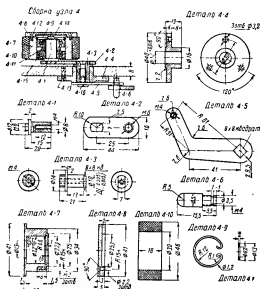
Прижимной ролик (узла 4) и его детали: 4-1—ось (сталь 45)—1 шт.; 4-2—малый рычаг (сталь 20-листовая толщиной 2 мм)—1 шт.; 4-3—ось рычага (сталь 45)—1 шт.; 4-4—подшипник (сталь 25)—1 шт.; 4-5—большой рычаг (сталь 20-листовая толщиной 2 мм)—1 шт.; 4-6—палец (сталь У8А)—1 шт.; 4-7—стакан (сталь 25)—1 шт.; 4-8—крышка (сталь 25)—1 шт.; 4-9—опорное кольцо (пруж. сталь марки Н)—1 шт.; 4-10—кольцо (резина средней твердости)—1 шт.; 4-11—распорное кольцо (сталь 3)—1 шт.; 4-12—винт М2×8 мм (сталь 3)—3 шт.; 4-13—винт М3×10 мм (сталь 3)—3 шт.; 4-14—винт М4×8 мм (сталь 3)—1 шт.; 4-15—шарикоподшипник с внешним диаметром 22 мм, внутренним—8 мм и высотой 7 мм—2 шт.; 4-16—винт М4×10 мм (сталь 3)—1 шт. Диаметр оси 4-1 (8 мм) должен быть подогнан под внутренний диаметр шарикоподшипника 4-15 в расчете на скользящую посадку
